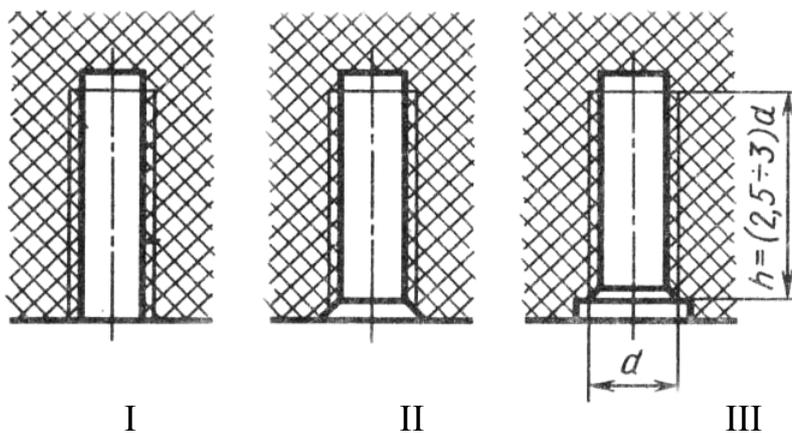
Формы резьбовых отверстий: I-неправильная с выходом витков резьбы на поверхность детали; II, III-правильные с заходной фаской и выборкой
